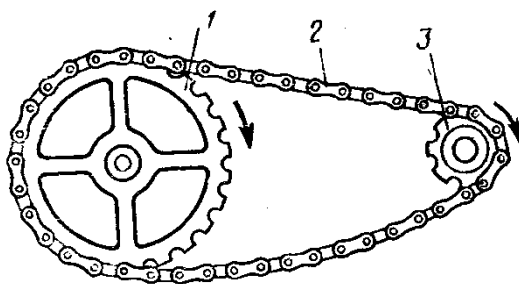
Цепная передача: 1 - ведомая звездочка; 2 – цепь; 3 - ведущая звездочка.
